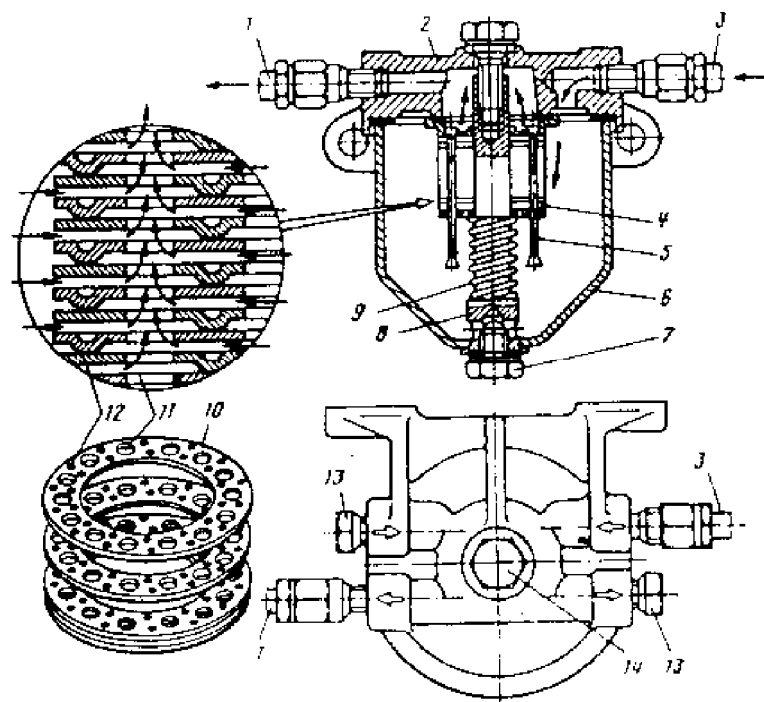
Фильтр-отстойник: 1-топливопровод, идущий к топливному насосу; 2-корпус-крышка; 3-топливопровод, идущий от топливного бака; 4-фильтрующий элемент; 5-стойка; 6-отстойник; 7-сливная пробка; 8-стержень фильтрующего элемента; 9-пружина; 10-пластина фильтрующего элемента; 11-отверстие в пластине для прохода очищенного топлива; 12-выступы на пластине; 13-заглушки; 14-болт крепления корпуса-крышки.
